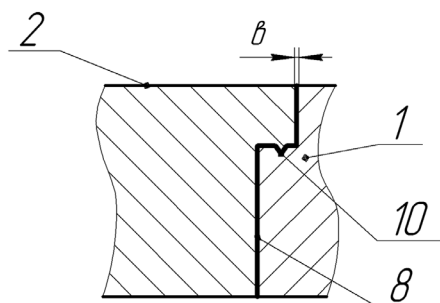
Вариант установки основания в корпусе матрицы: 1 – корпус матрицы; 2 – основание; 3–7, 9 – см. рис. 4; 8 – зазор; 10 – выступ; b – ширина температурного зазора
